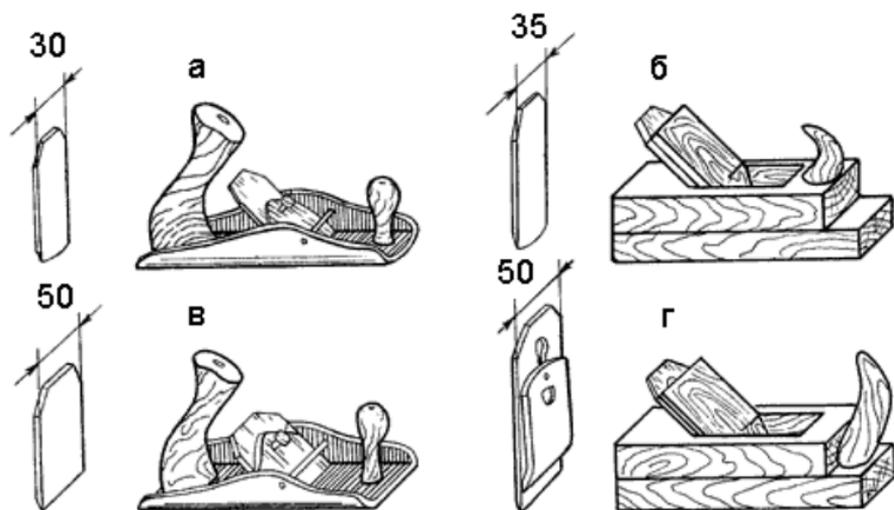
Ручные инструменты: а – шерхбель деревянный; б – шерхбель металлический; в – рубанок деревянный; г –
